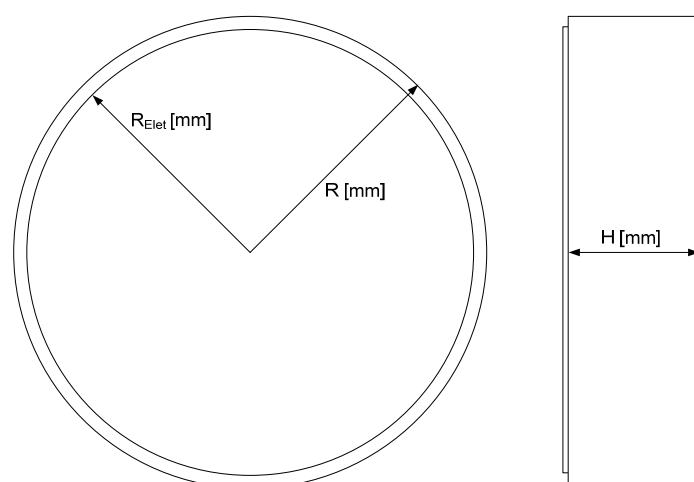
Planta e corte de um resistor a óxido metálico genérico
